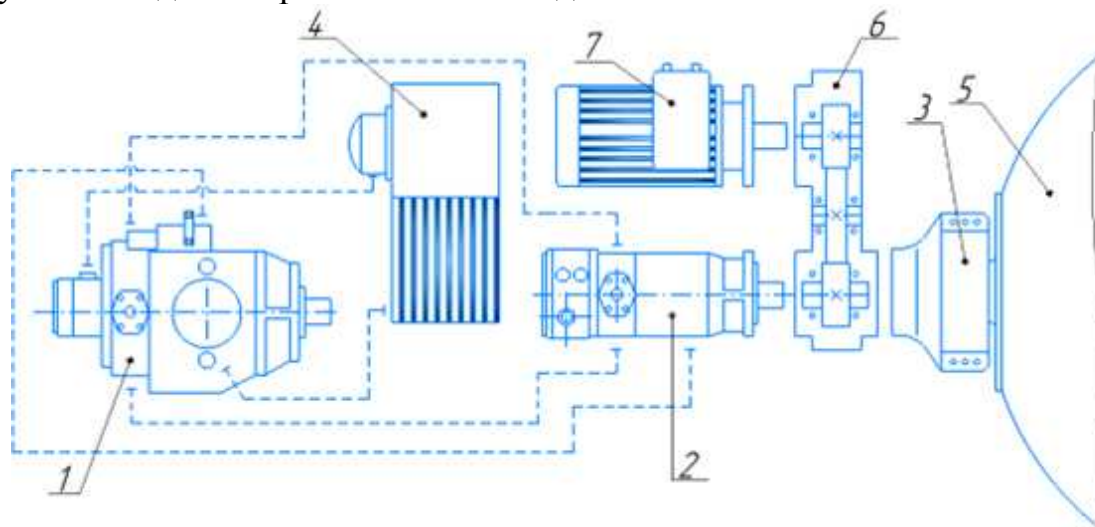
Схема установки электромотора через раздаточный редуктор.
